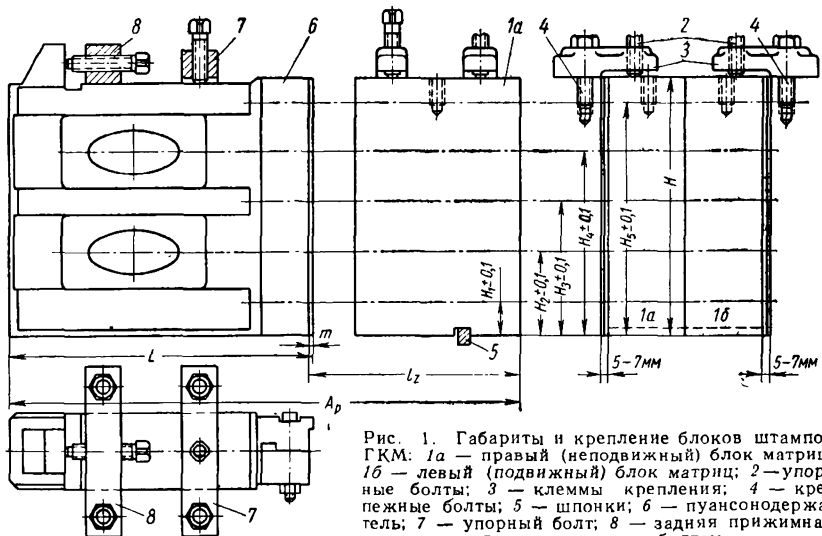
Габариты и крепление блоков штампов ГКМ: 1а — правый (неподвижный) блок матриц; 1б — левый (подвижный) блок матриц; 2 — упорные болты; 3 — клеммы крепления; 4 — крепежные болты; 5 — шпонки; 6 — пуансондержатель; 7 — упорный болт; 8 — задняя прижимная планка с упорным болтом
